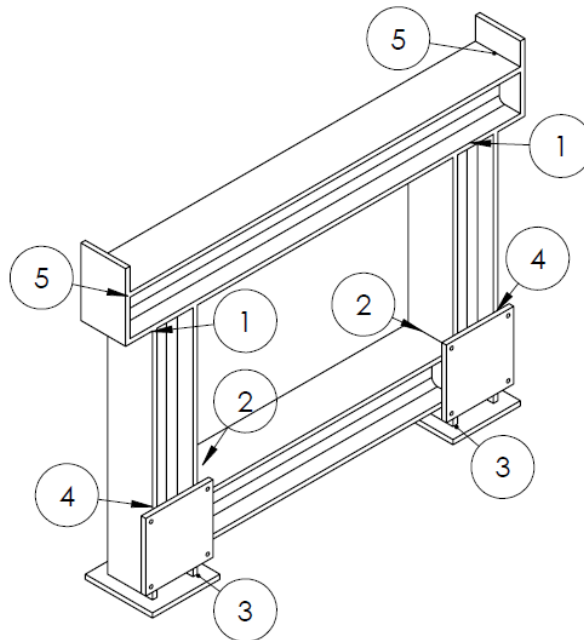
Uniones de soldadura en la bancada.
